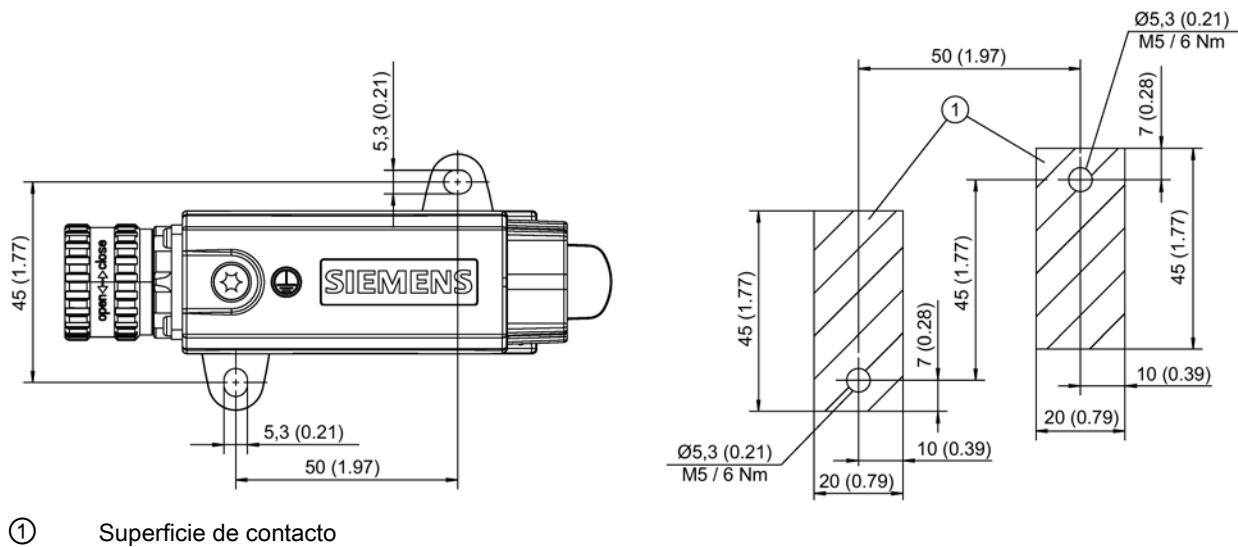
Plantilla de taladrado para el montaje SME20/SME25
